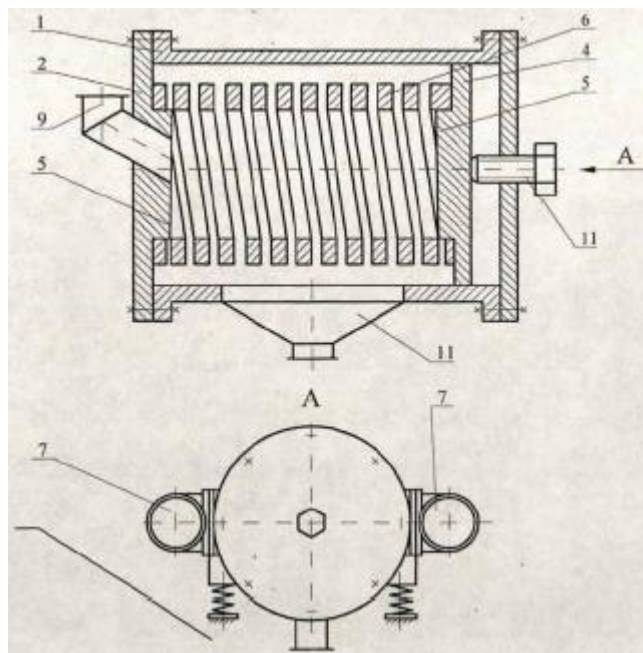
Конструкция вибрационной мельницы (а.с. №871820): 1- корпус, 2- левая крышка, 3- правая крышка, 4 –подвижная крышка, 5 – шейка, 6 – помольная камера, 7 – вибропривод, 8-пружины, 9 – загрузочный патрубок, 10 – выгрузочный патрубок, 11- винт
